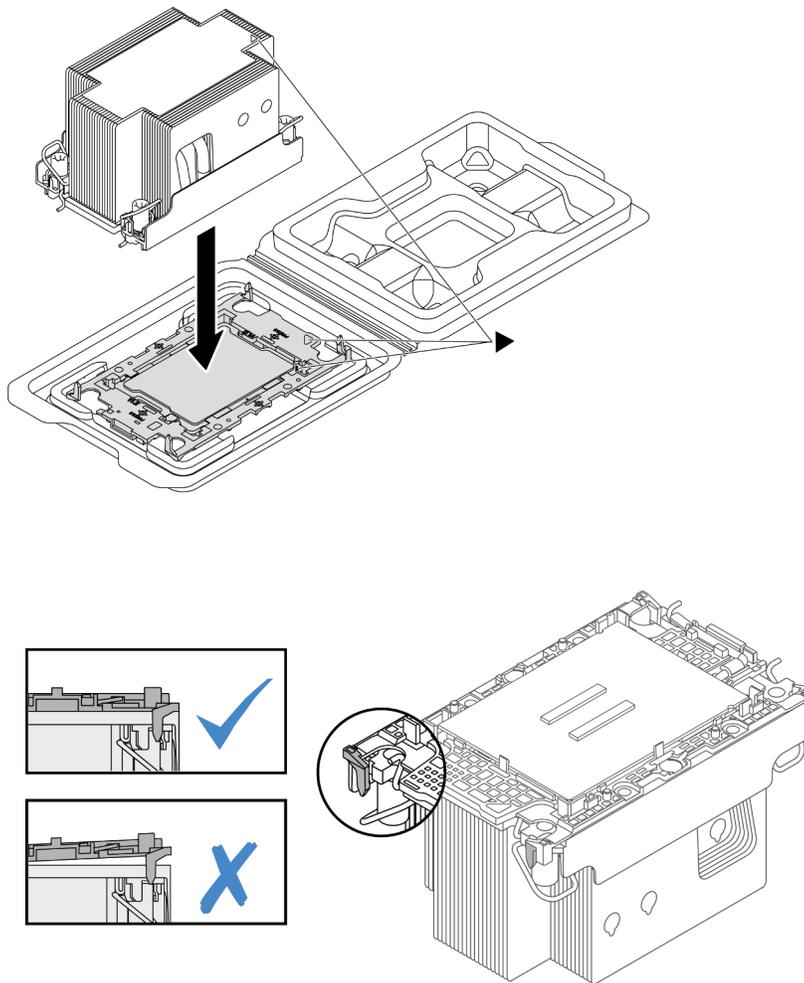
Assemblage du module de processeur-dissipateur thermique avec le processeur dans le plateau d'expédition
